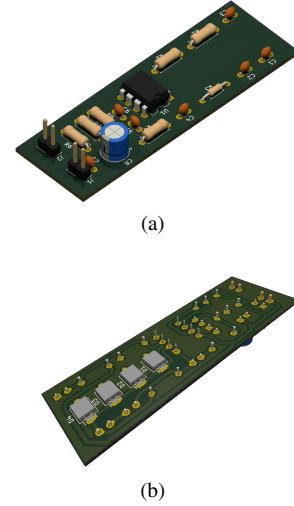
Modelado 3D del PCB. (a) Parte frontal, (b) parte posterior
